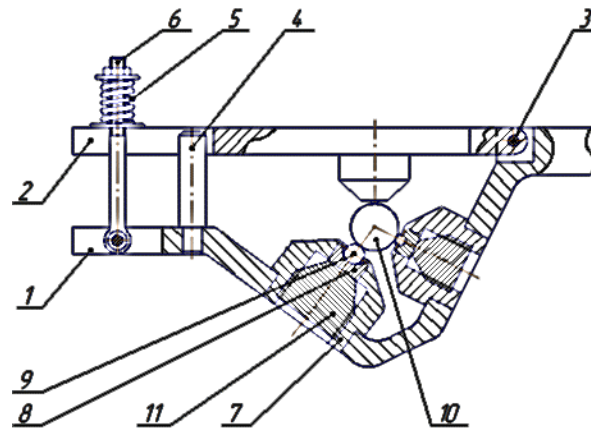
Загальний вид обкатника. 1 – основа, 2 – рухомий важіль, 3 – вісь важеля, 4 – напрямний штифт, 5 – пружина, 6 – відкидний болт з гайкою, 7 – корпус, 8 – кулькова опора, 9 – кулька, 10 – деталь, що обробляється, 11 – гвинтовий притиск.
